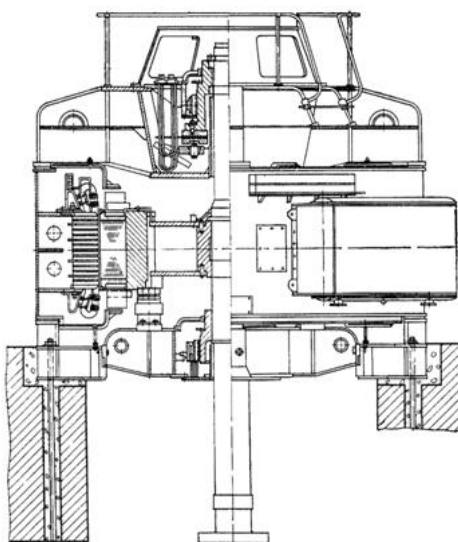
Внешний вид двигателей типа ВДС.
